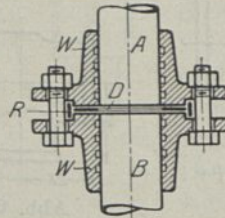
Flanschenverbindung mit Dichtungsschutzring.
